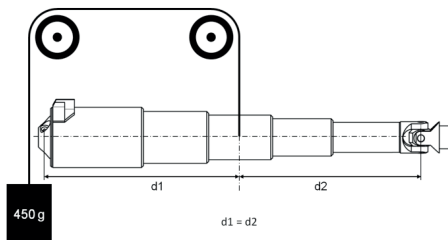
Schema Messaufbau Teleskop-Durchbiegung
